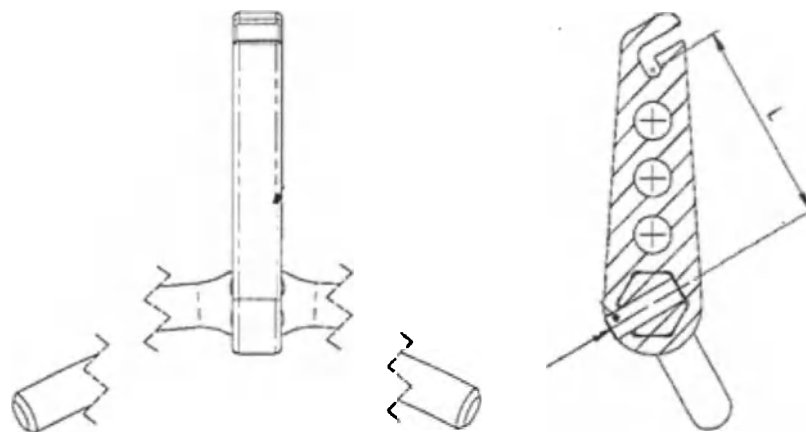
Балка стяжки поперечной MUST MINI с двумя зажимами длиной 8 мм; Балка стяжки поперечной MUST MINI с двумя зажимами длиной 12 мм; Балка стяжки поперечной MUST MINI с двумя зажимами длиной 16 мм;
